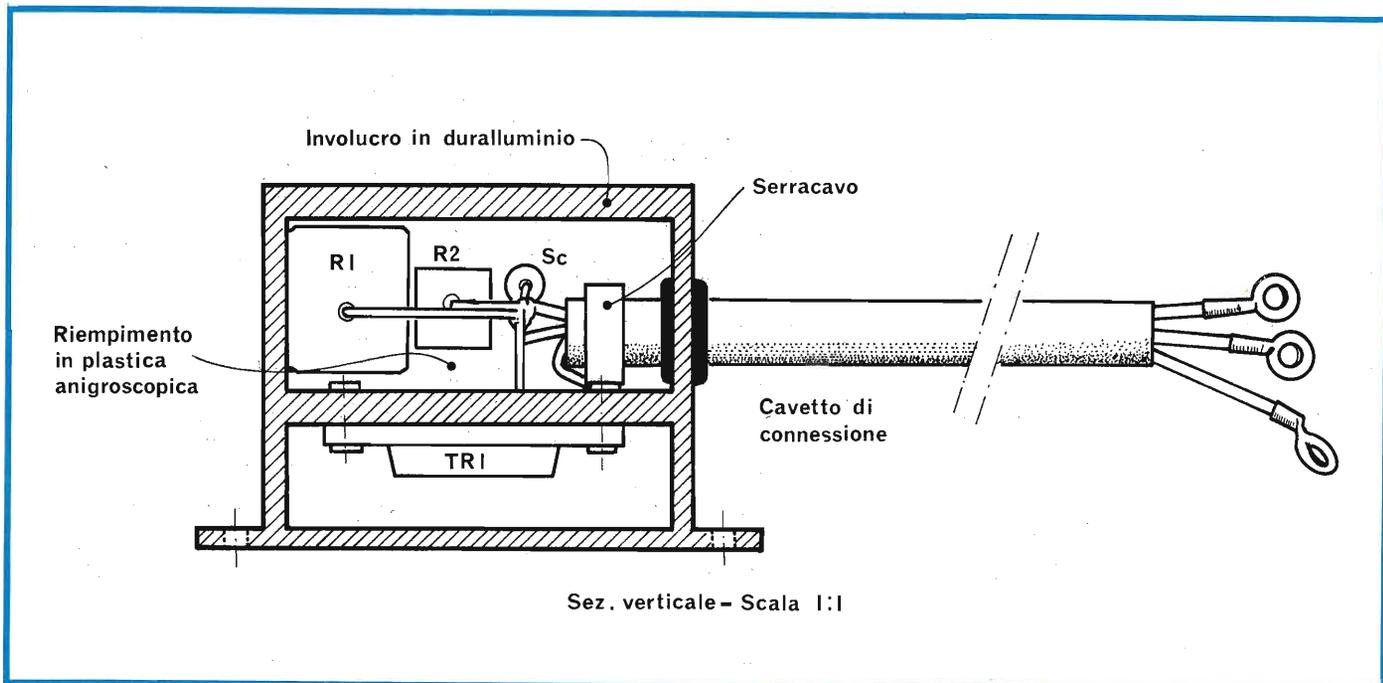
Sezione verticale dell'accensione di figura 7.
